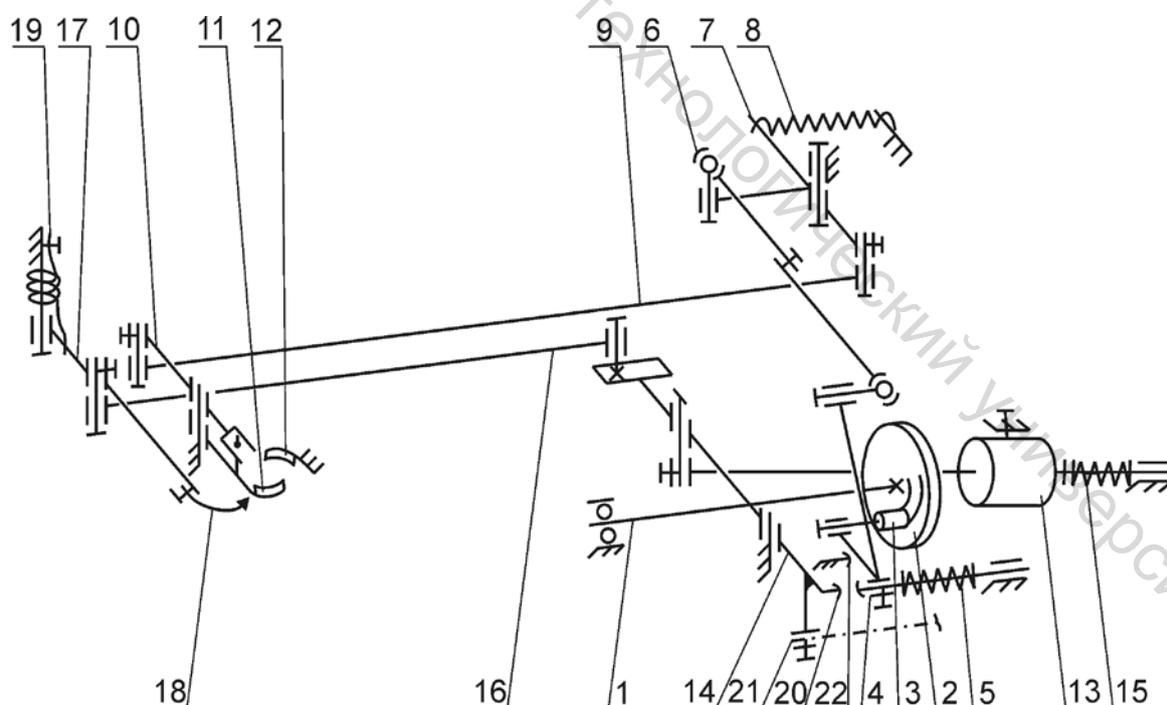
Кинематическая схема механизма обрезки машины DDL-9000B
